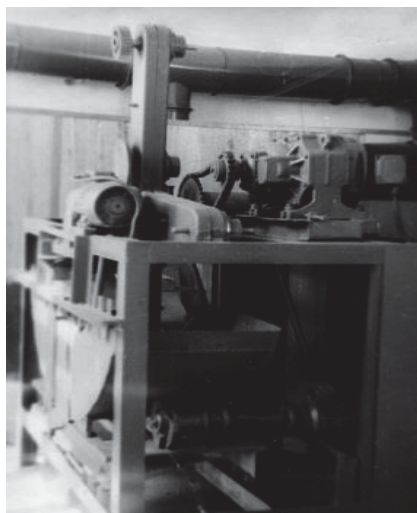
Образец станка для отделочно-зачистной и упрочняющей обработки шестерен с помощью совмещения их сложного движения с колебательным движением рабочих тел
